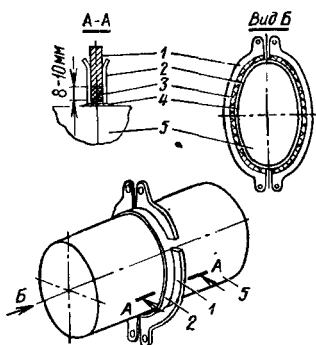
Получение конфигурации рубильника сборочного приспособления:
